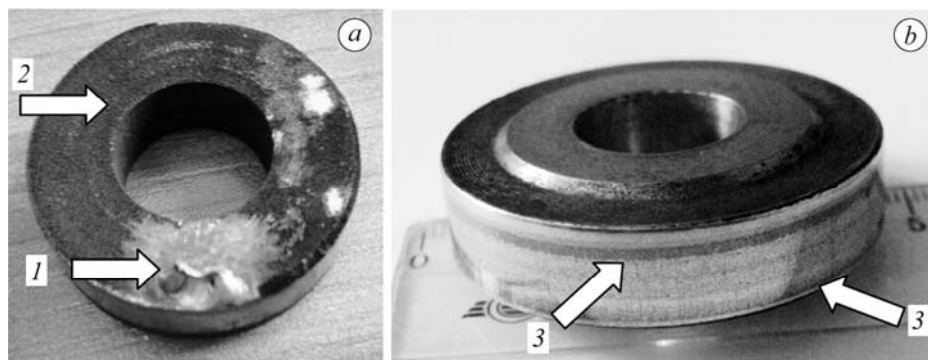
Сталеві ролики після випробувань: *a* – сплав № 1; *b* – сталь 1.0503. 1 – місце, де був припаяний пристрій для фіксування ролика; 2 – поверхня ролика, що зазнала водневої корозії; 3 – смуги чорного кольору, які утворились на поверхні тертя під час експерименту.
